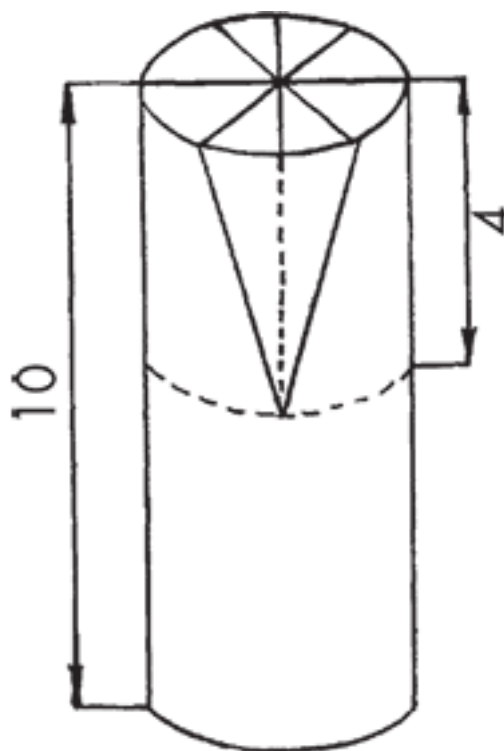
Разметка заготовки при изготовлении деревянного колунка
